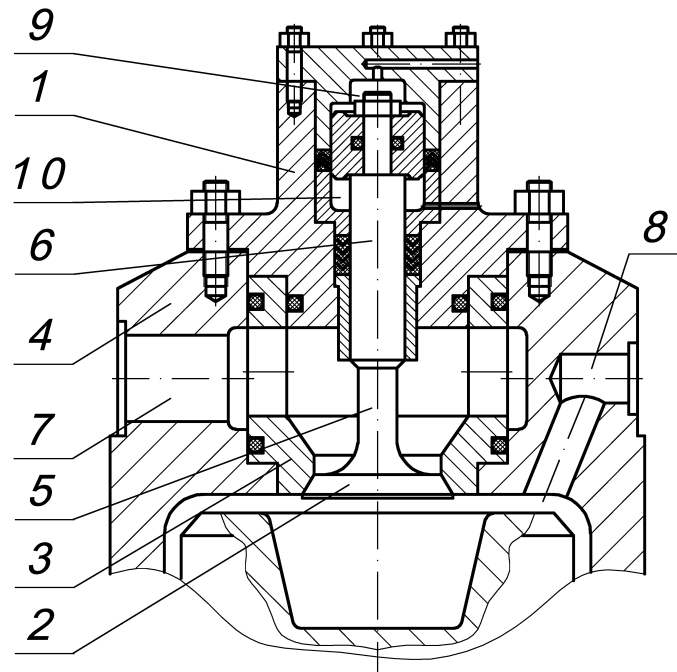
Наповнювально-зливний вузол гідравлічного преса [286]
